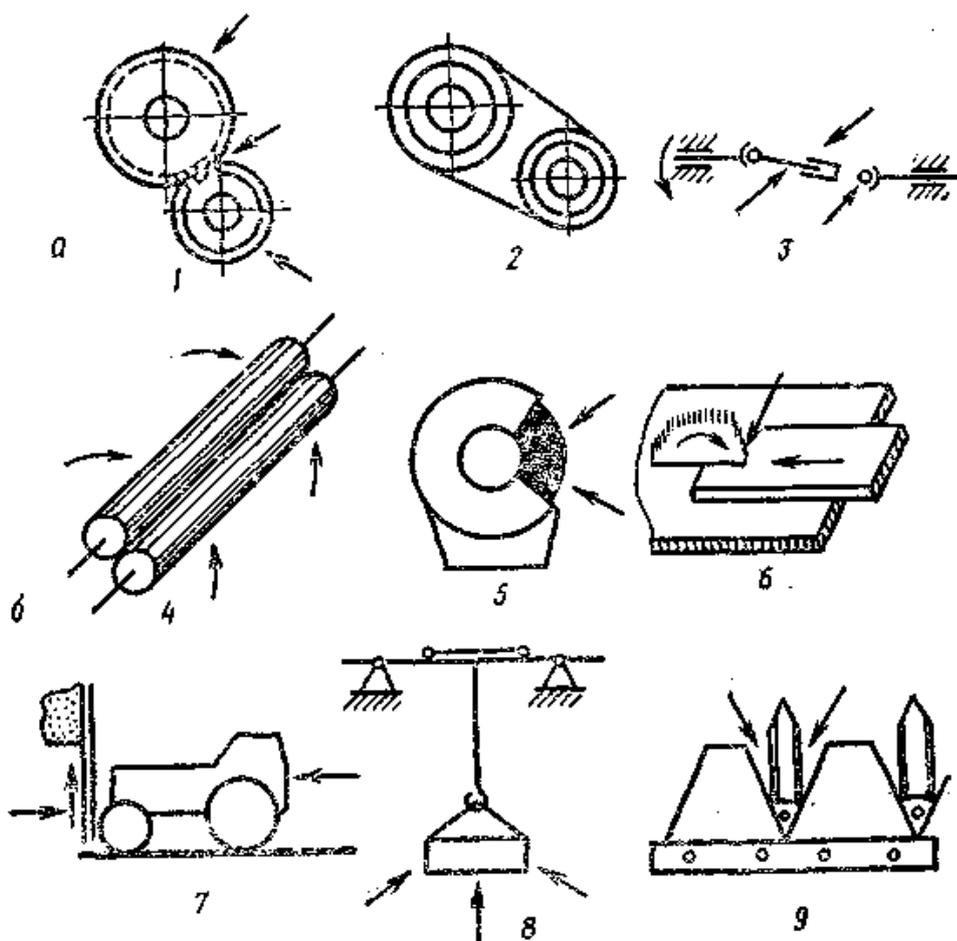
Опасные зоны в: 1 – шестеренчатой передаче; 2 – ременной передаче (цепной); 3 – карданной передаче; 4 – вращающихся вальцах; 5 – наждачном станке; 6 – дисковой пиле; 7 – тракторе со стогометателем; 8 – грузоподъемном механизме; 9 – режущем аппарате; а – опасные зоны, постоянные в пространстве; в – опасные зоны, переменные в пространстве
